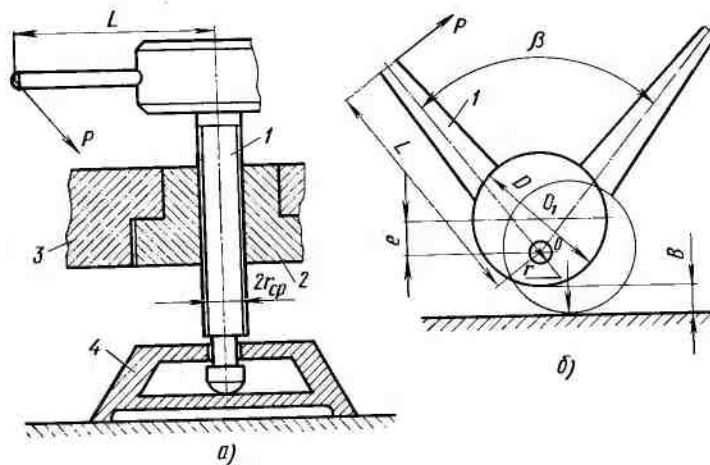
Зажимные устройства: а — винтовой зажим; 1 — винт, 2 — втулка, 3 — корпус, 4 — пята; б — эксцентриковый зажим; 1 — рукоятка эксцентрикового зажима
